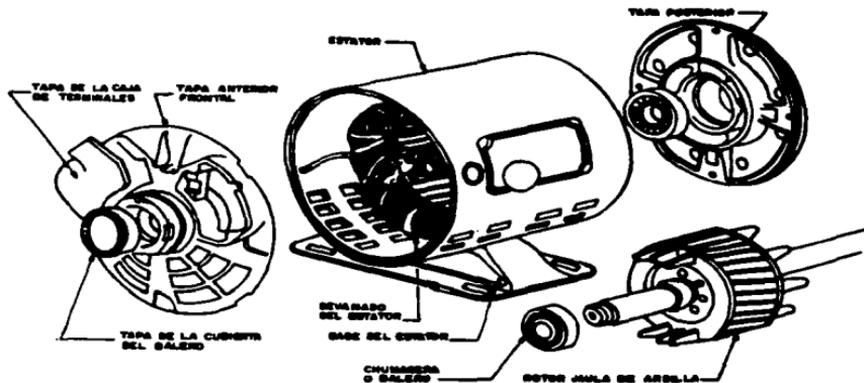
Vista de los principales componentes de un motor de inducción.
